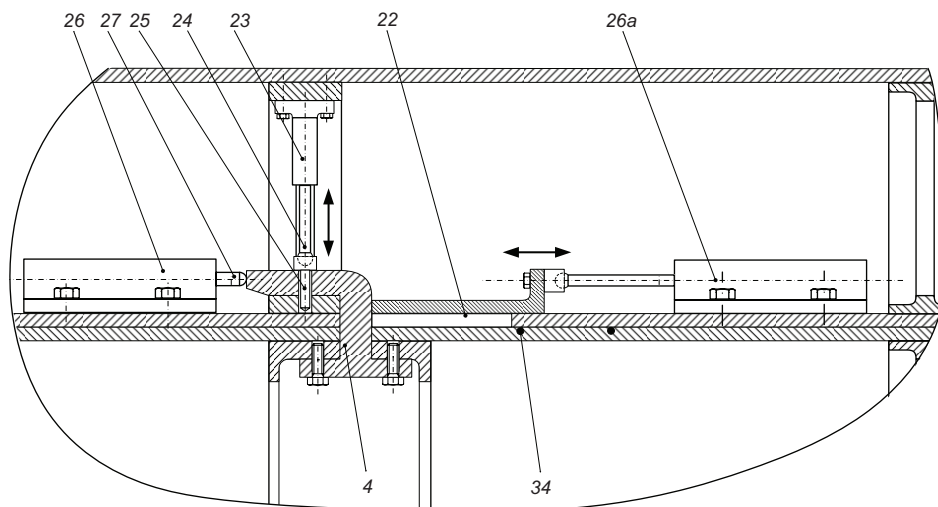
Механізми для сполучення і розстикування верхньої і нижньої частин фюзеляжу літака
